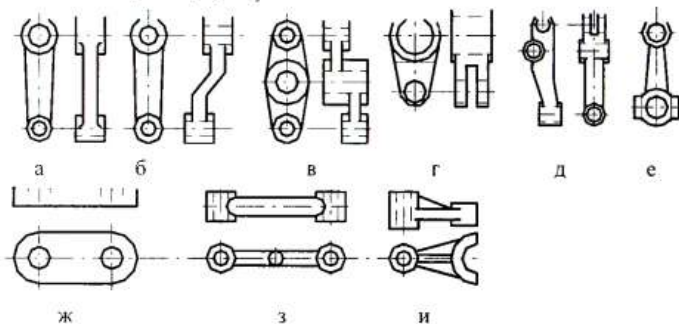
Конструктивні різновиди важелів: а – прямий; б – вигнутий; в – з центральним отвором; г – вильчатий; д – з пересічними вісями; е – з різною головкою; ж – серга; з – тяга; и – вилка перемикачя
